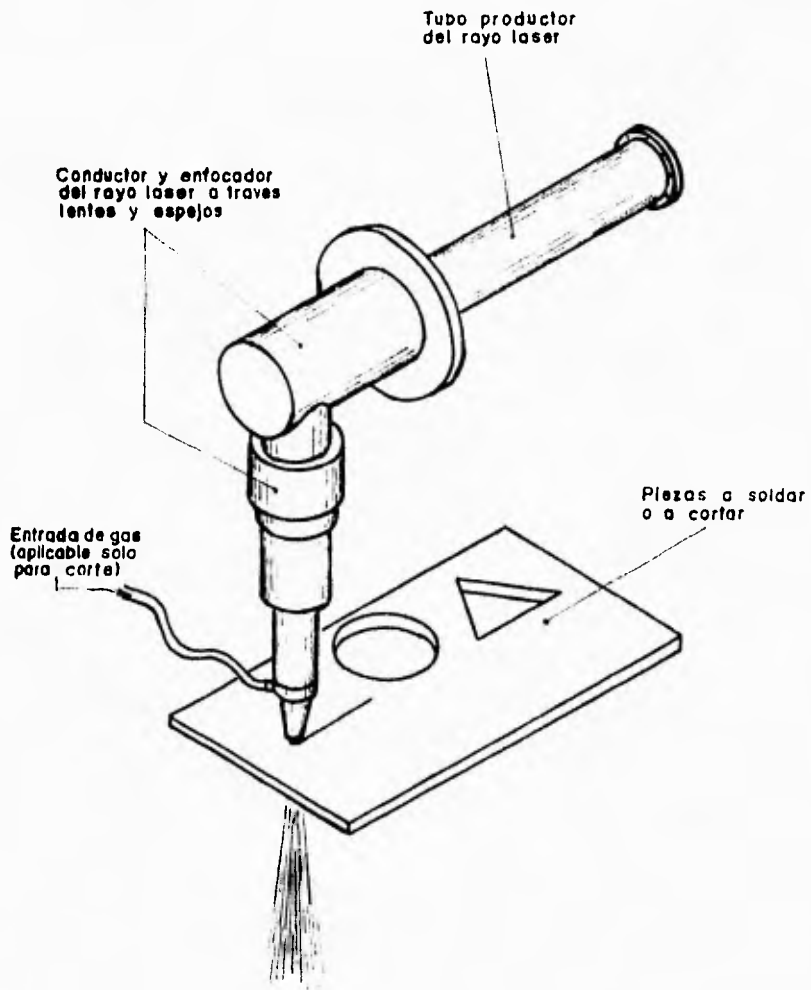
Soldadura por rayo laser (LBW)
